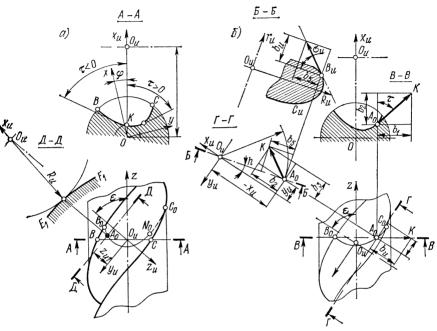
Схемы взаимного расположения обрабатываемой заготовки и производящего инструмента
